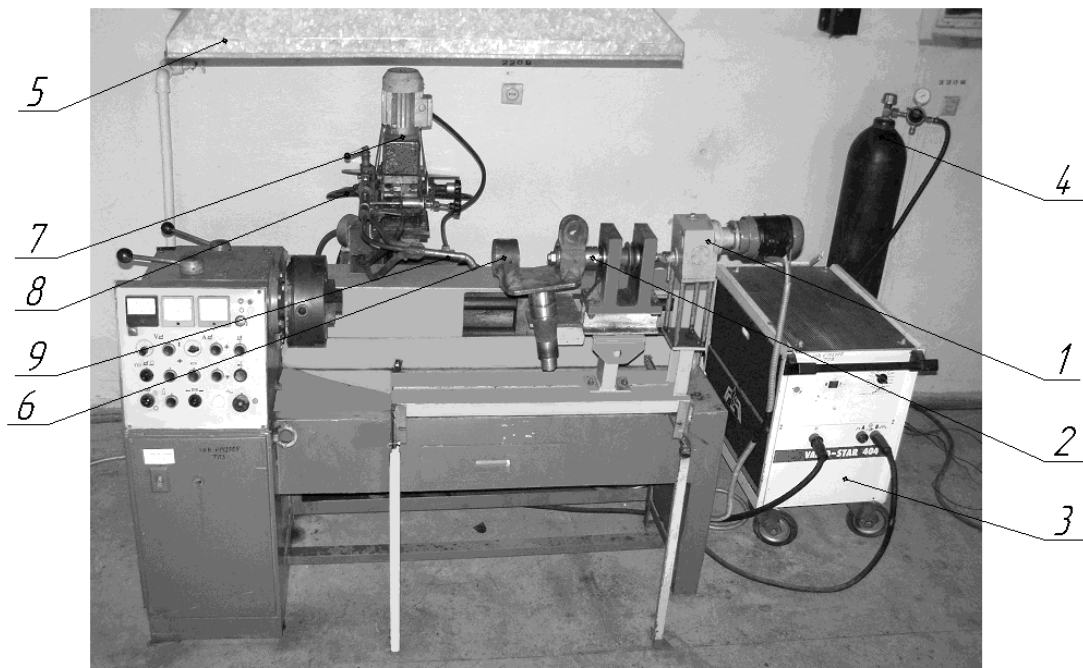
Установка для наплавки отверстий поворотной цапфы троллейбуса ЗИУ-9:
